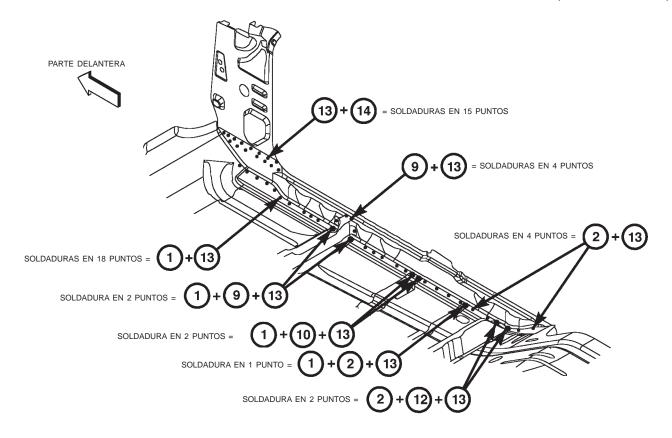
LARGUEROS DELANTEROS - LOCALIZACIONES DE LA SOLDADURA
